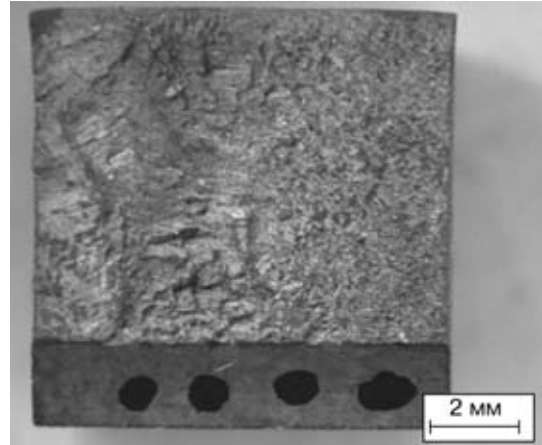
Общий вид поверхности излома пробы, содержащей сварной WIG шов после испытания на ударную вязкость. Перед испытанием пробы — низкотемпературная выдержка (700 °С, 100 ч)
